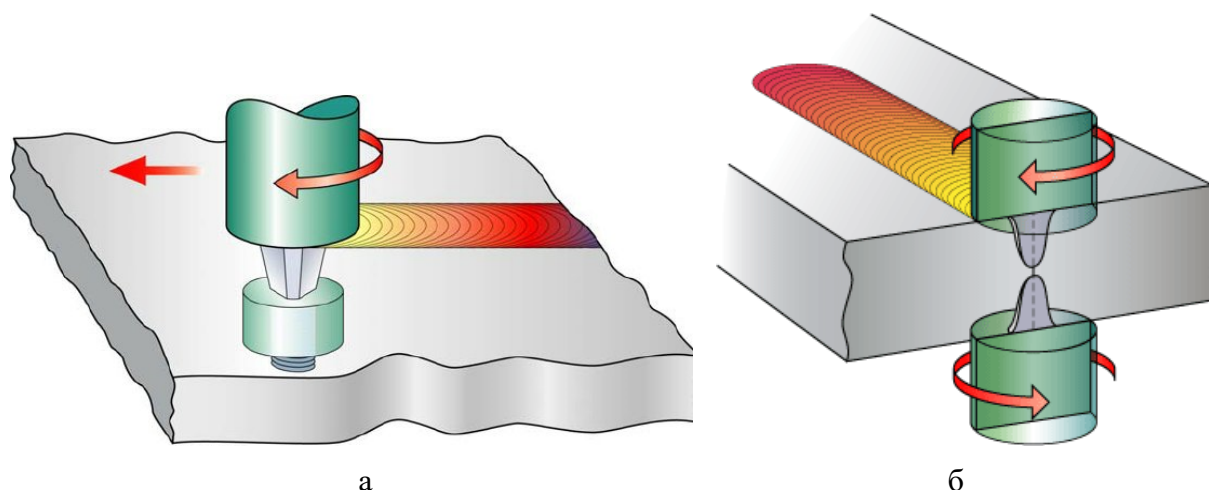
Схема СТП по технологии Bobin Stir Welding (а) [5] и двухсторонней синхронной сварки с разнонаправленным вращением инструментов (б) [6]
